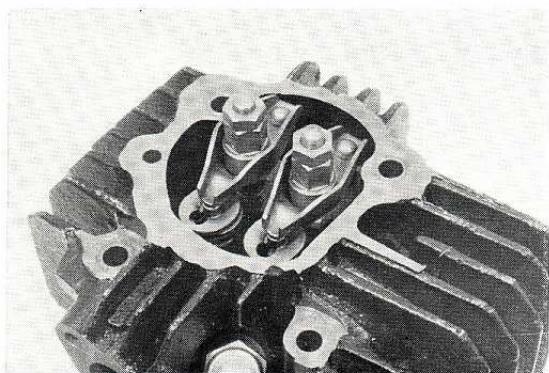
DEMONTAGE DU CULBUTEUR.
